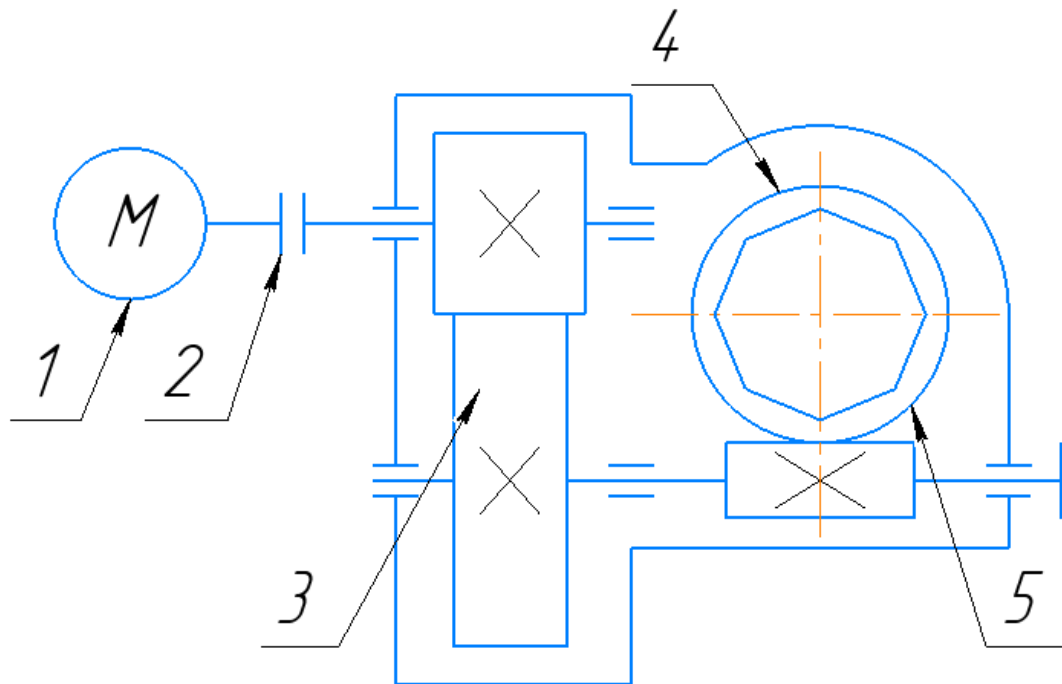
Кинематическая схема червячного цилиндрического редуктор (Amigo 2)
